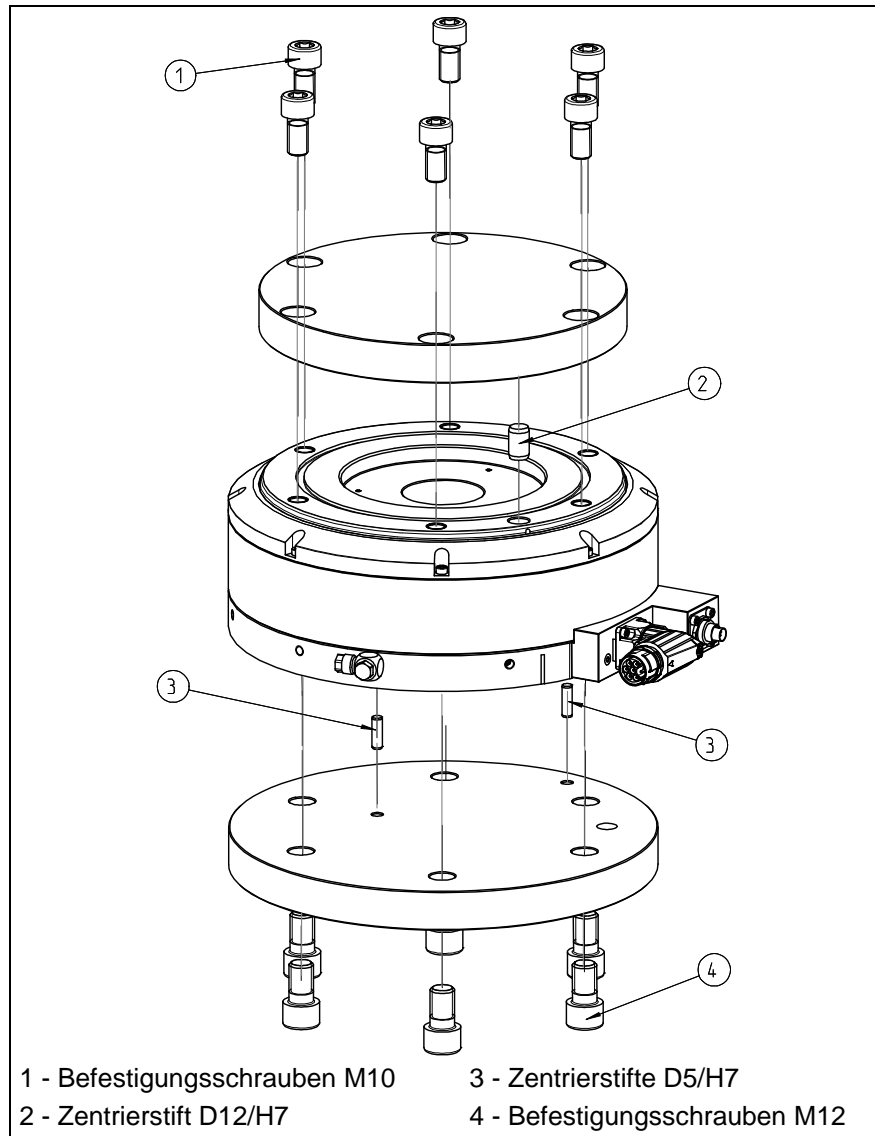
Ansicht Montage der Adapterplatten am Rotor und Grundträger
